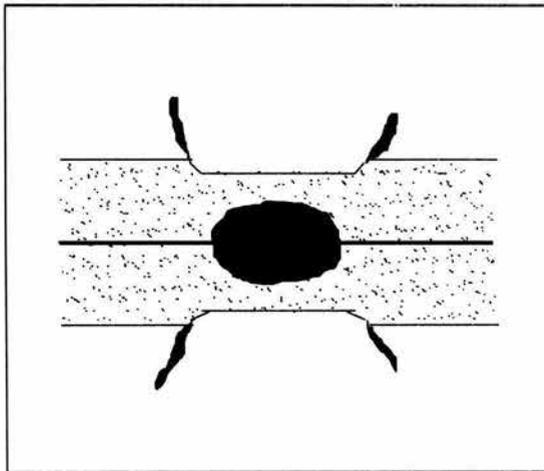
Soldadura incorrecta con expulsión de material sobre las láminas.
